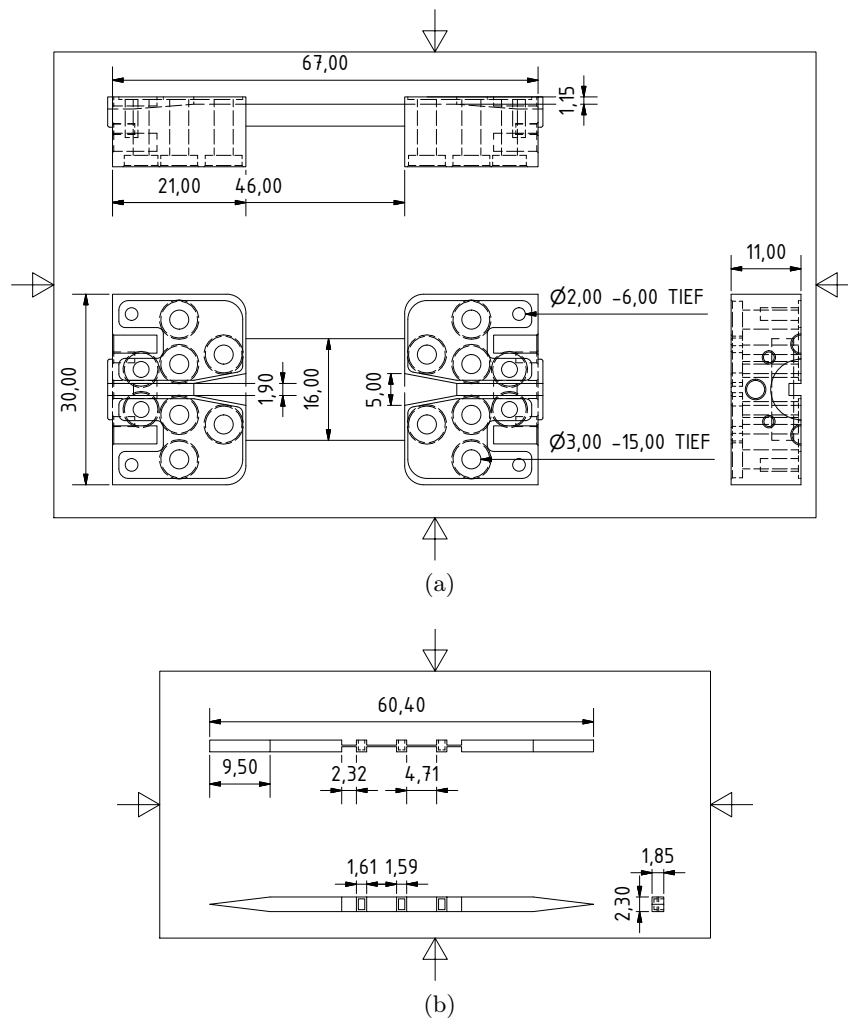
Zeichnungen (a) Messing Splitblocks und (b) des Rexolite-Einsatzes, mit den wichtigsten Dimensionen in mm.
